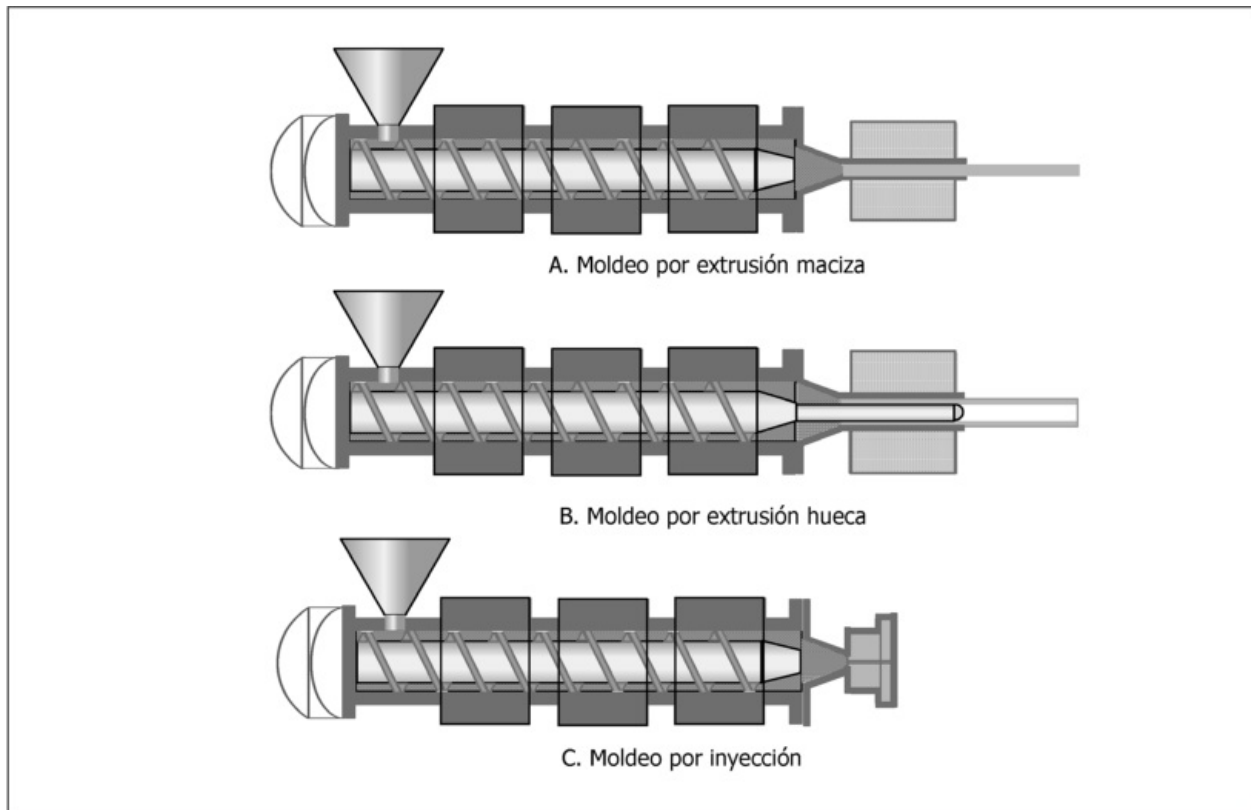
Máquinas de fabricación de plásticos por extrusión y moldeo por inyección.
